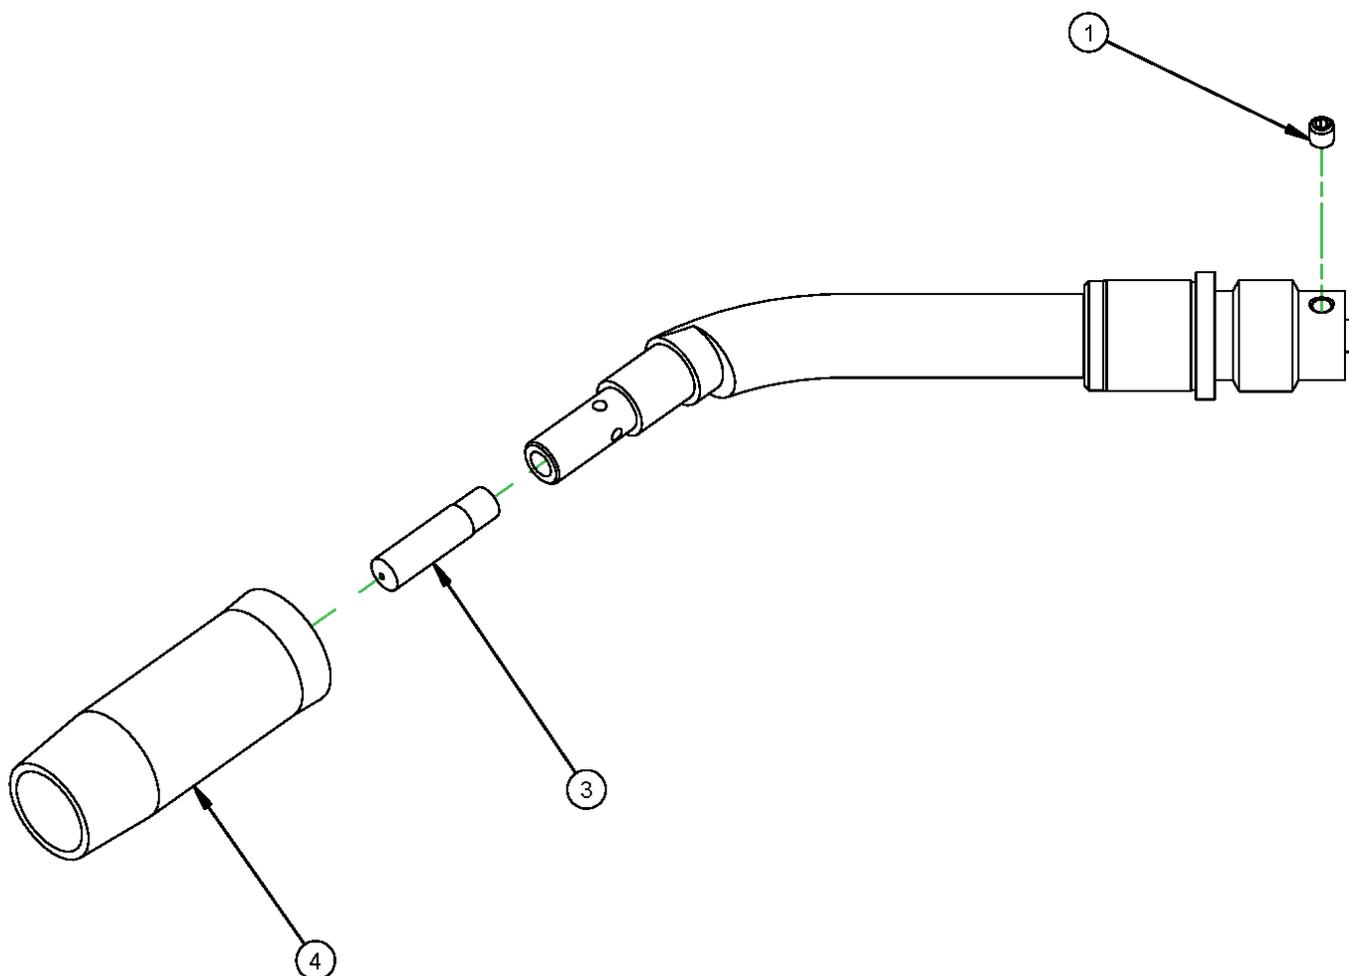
ЦИРКУЛЬНАЯ ГОРЕЛКА ДЛЯ ОБРАБОТКИ ВНЕШНИХ ДИАМЕТРОВ В СБОРЕ (КАТ. № 81384)
